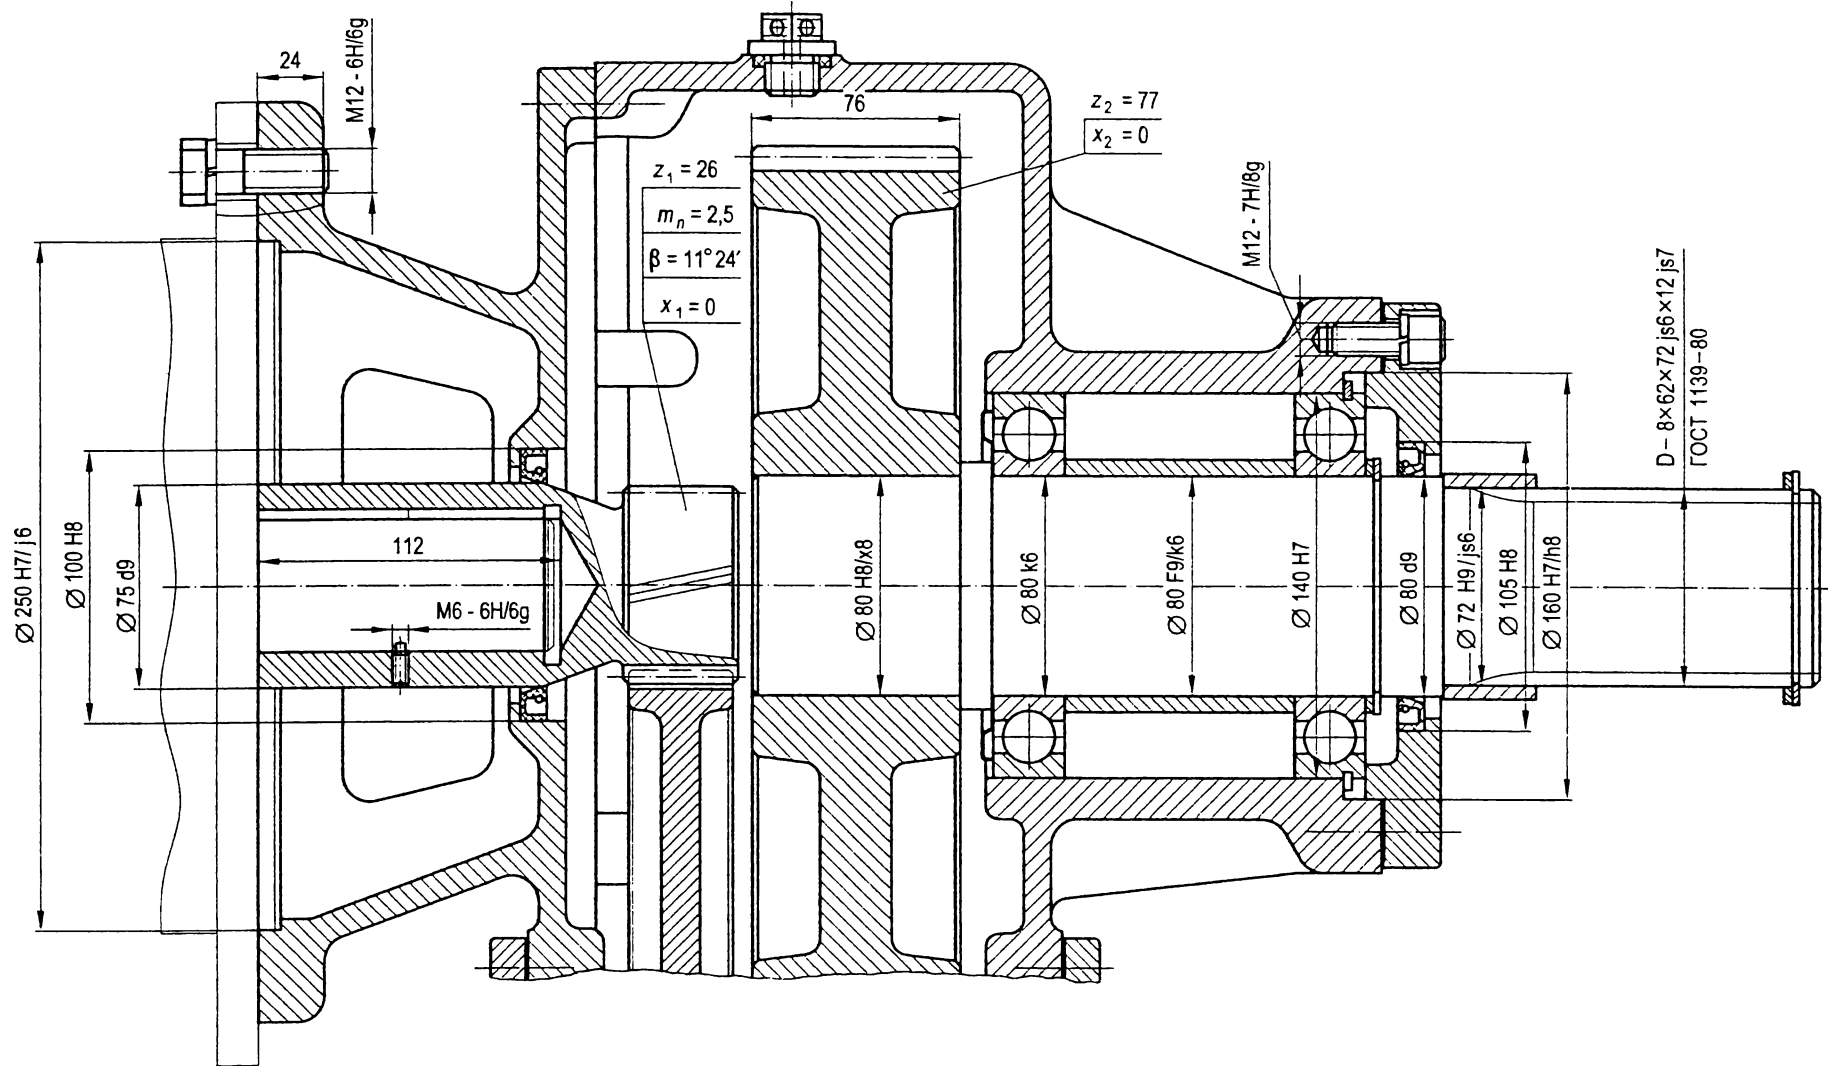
Пример конструкции тихоходного вала цилиндрического двухступенчатого вертикального зубчатого мотор-редуктора [1]
